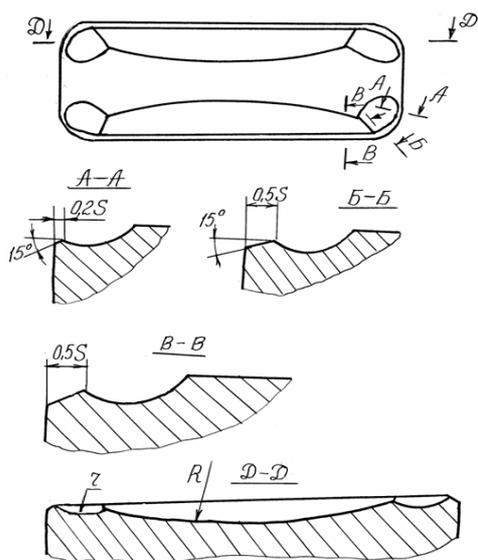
Эскиз пластины формы LNUX301940 с канавками эллиптической формы и лунками, копирующими форму передней поверхности износа
